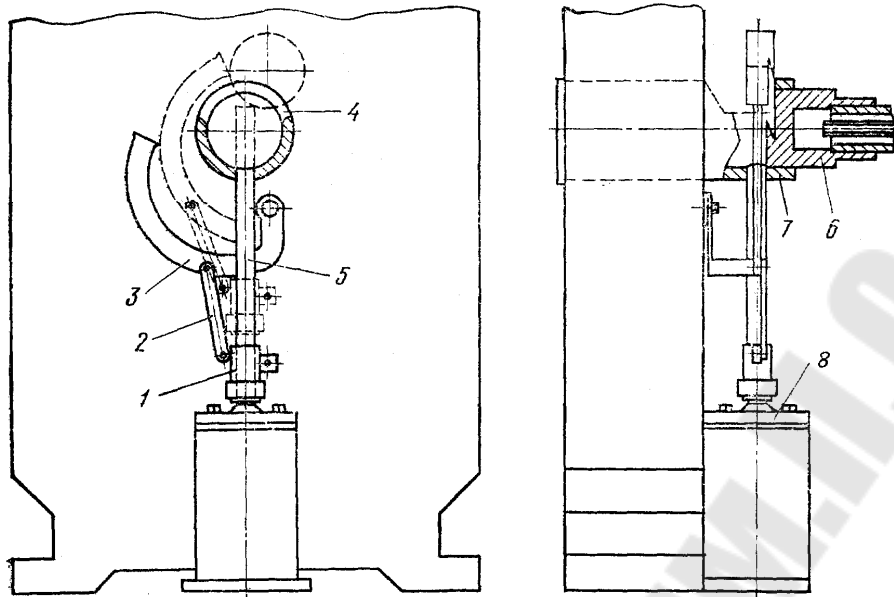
Устройство для сбрасывания пресс-остатка
